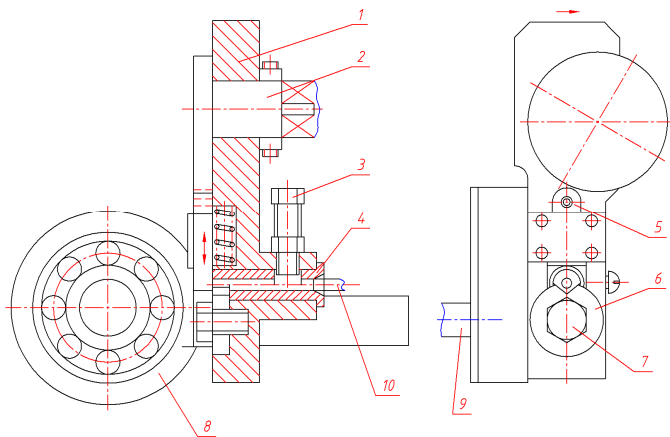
Пристрій для навивання пружин різних типорозмірів
